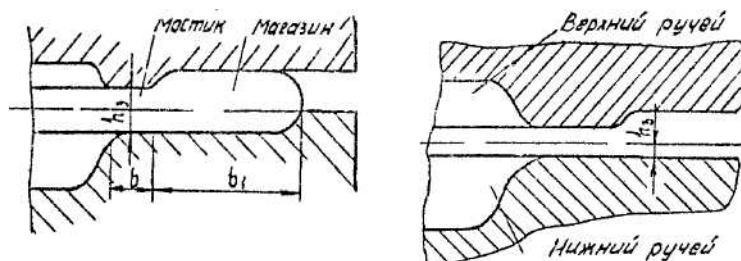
Конструкции облойной канавки: а) для молотового штампа; б) для штампа КРШП
